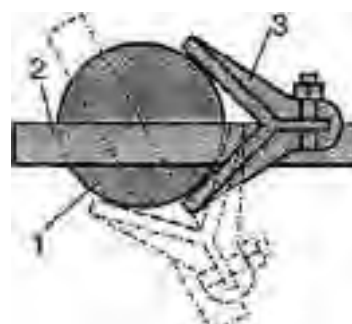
ЗНАХОДЖЕННЯ ЦЕНТРА ТОРЦЯ ЗАГОТОВКИ КОСИНЦЕМ-ЦЕНТРОШУКАЧЕМ
